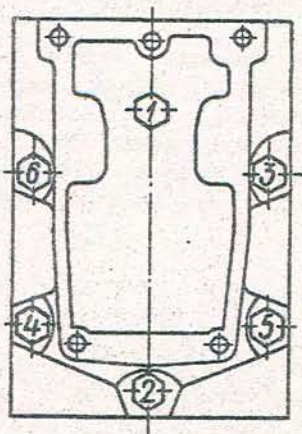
Порядок затяжки болтов крепления головок цилиндров.
